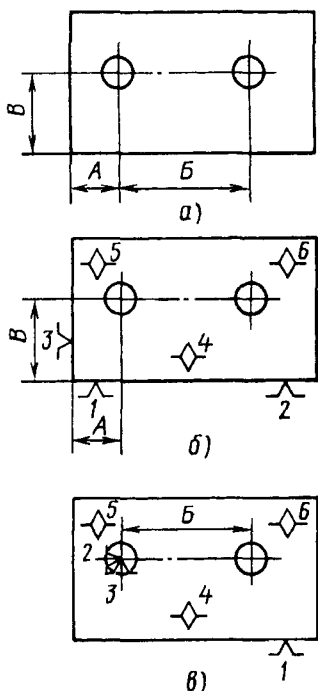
Схемы базирования заготовки корпусной детали: а – эскиз детали; б – по трем плоскостям; в – по отверстию и плоскостям на второй операции
